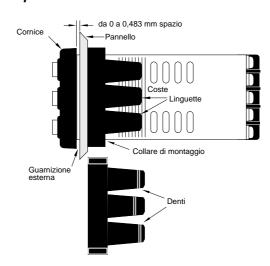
Visione posteriore della copertura esterna ed esempio di dispositivo di protezione IP65/NEMA 4X.
